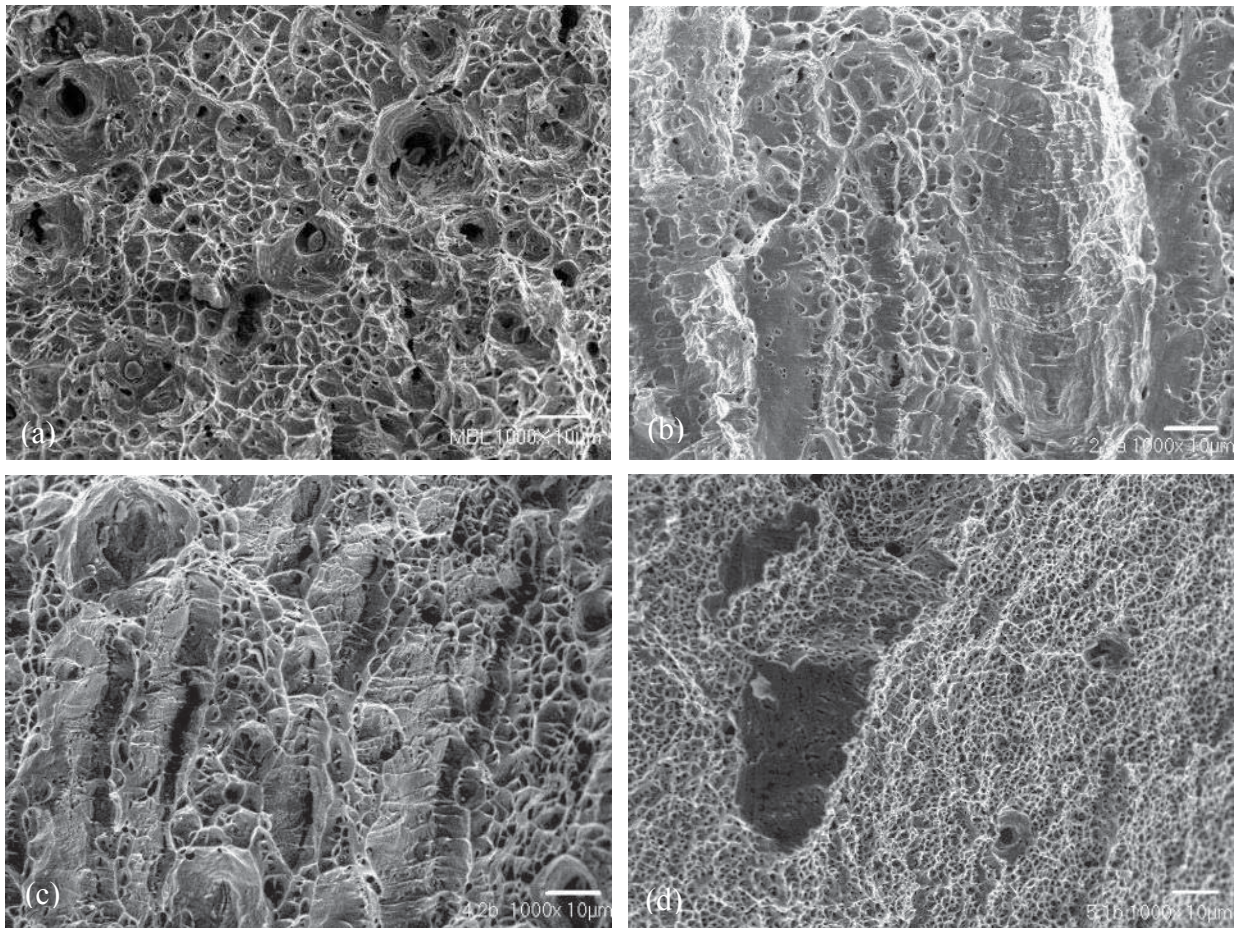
Fractografías del ensayo de tensión con unión en simple V 1000x (a) Material base (b) ZAT, soldada sin campo magnético (c) ZAT, soldada con campo magnético (d) ZAT, soldada con campo magnético y variando la orientación del la líneas del campo.
